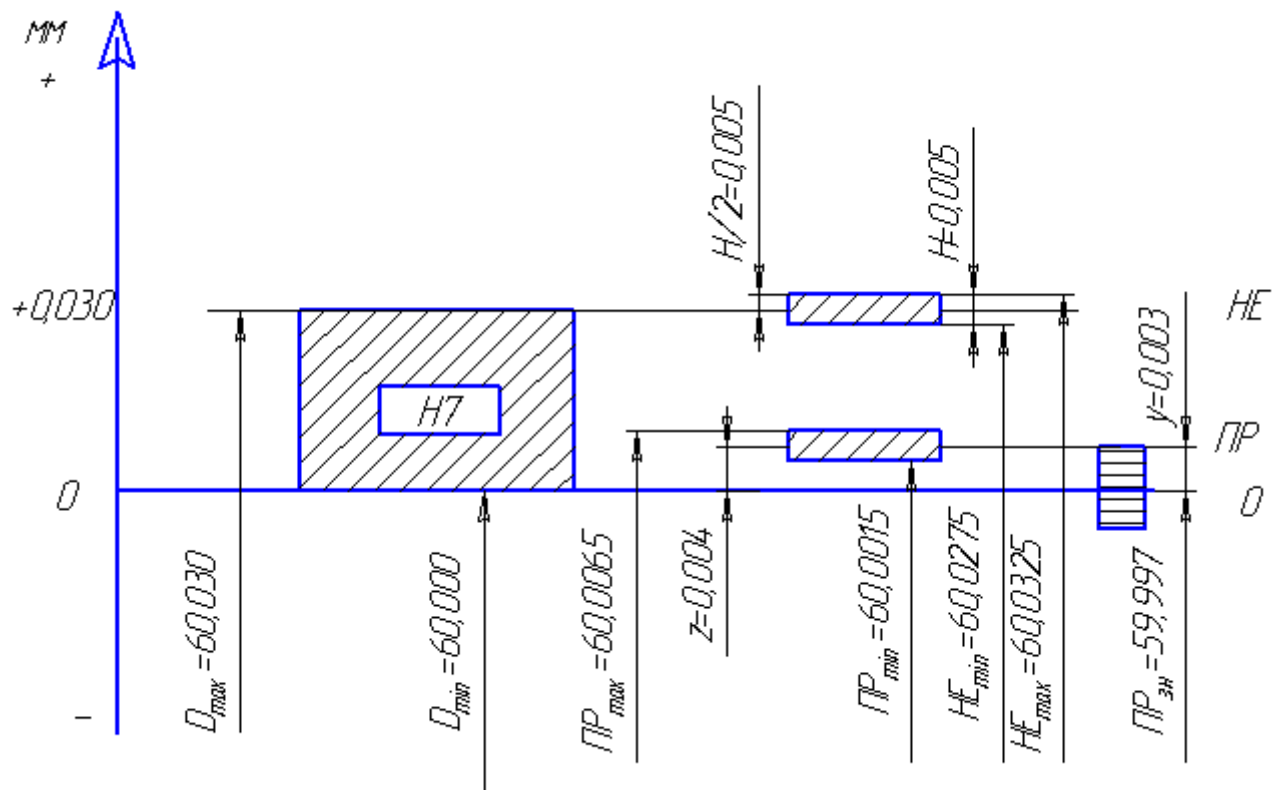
Схема розміщення полів допусків на виготовлення калібра - пробки для контролю отвору  $\varnothing 60H7$
